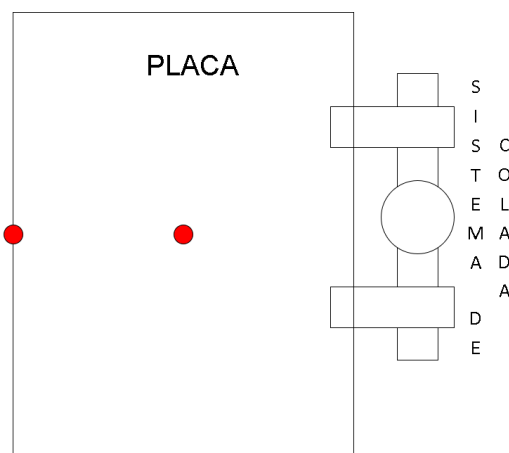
Vista superior de las placas fabricadas y su sistema de colada.
